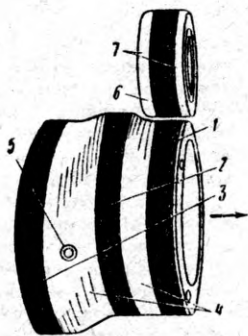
Вал газораспределения с роликом: 1, 2 — профили переднего хода (для номинальных и пониженных оборотов); 3 — профиль заднего хода; 4 — переходные поверхности; 5 — отверстие для подключения гидравлического сервоустройства; 6 — рабочий профиль кулачка; 7 — коническая фаска.
